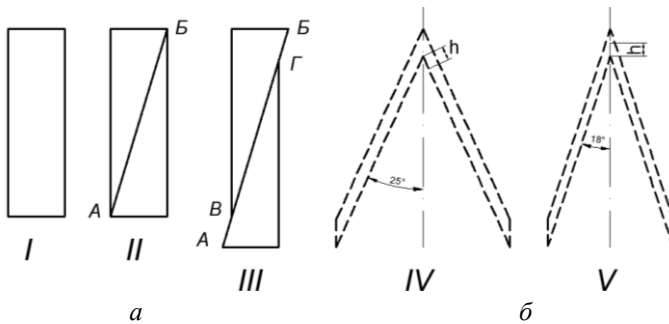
Розпускання пластини (а) та схема розташування клиноподібної смужки шкурки (б):
